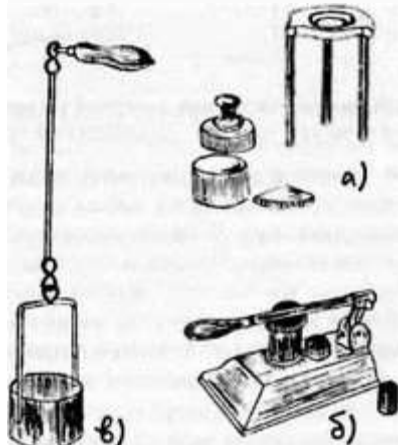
Аппараты для литья сплавов металлов: а) - Бибера, б) - Зольбрш-Платшека, в) - ручная центрифуга
